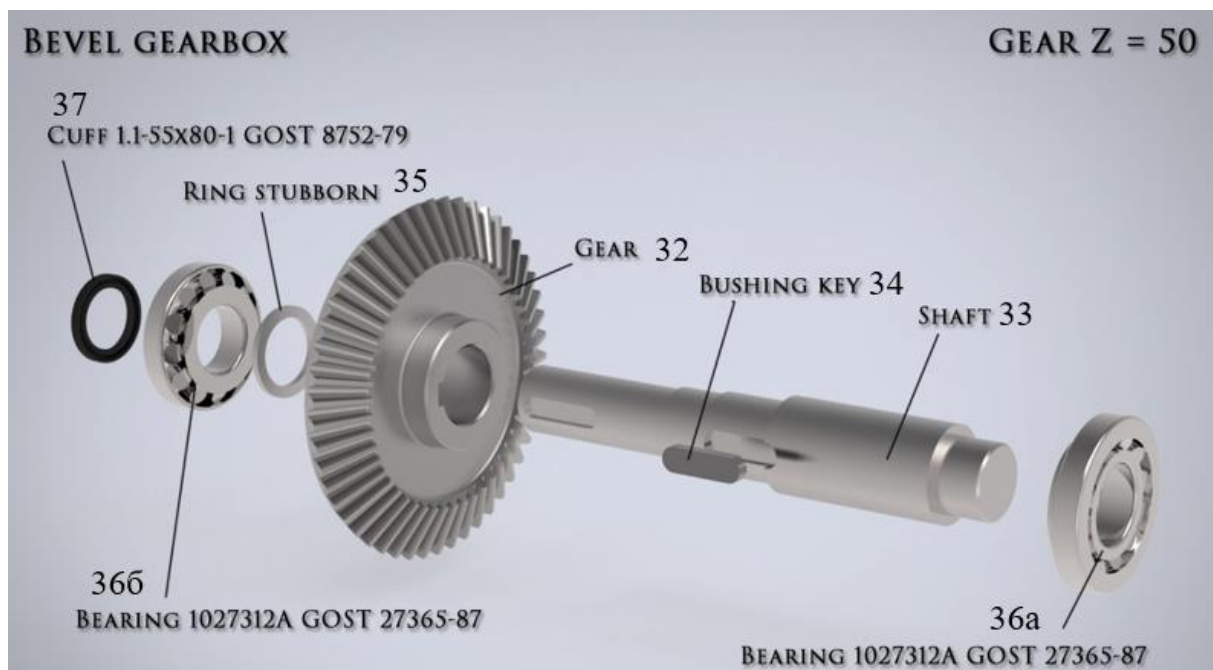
Вал ведучий редуктора конічного одноступінчастого [59]
